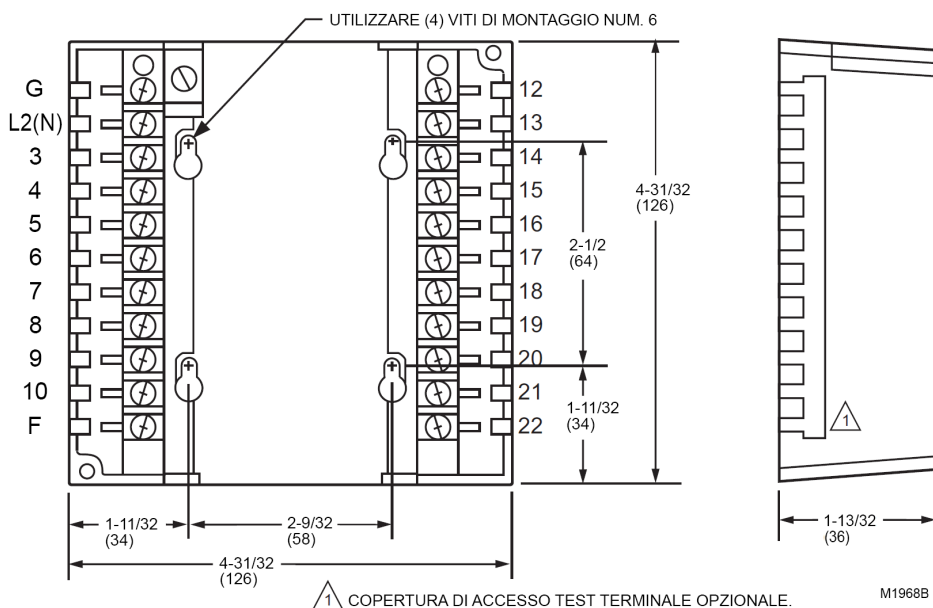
Vista superiore e frontale della sottobase di cablaggio Q7800A1005 (2 lati) con dimensioni in pollici (mm).
